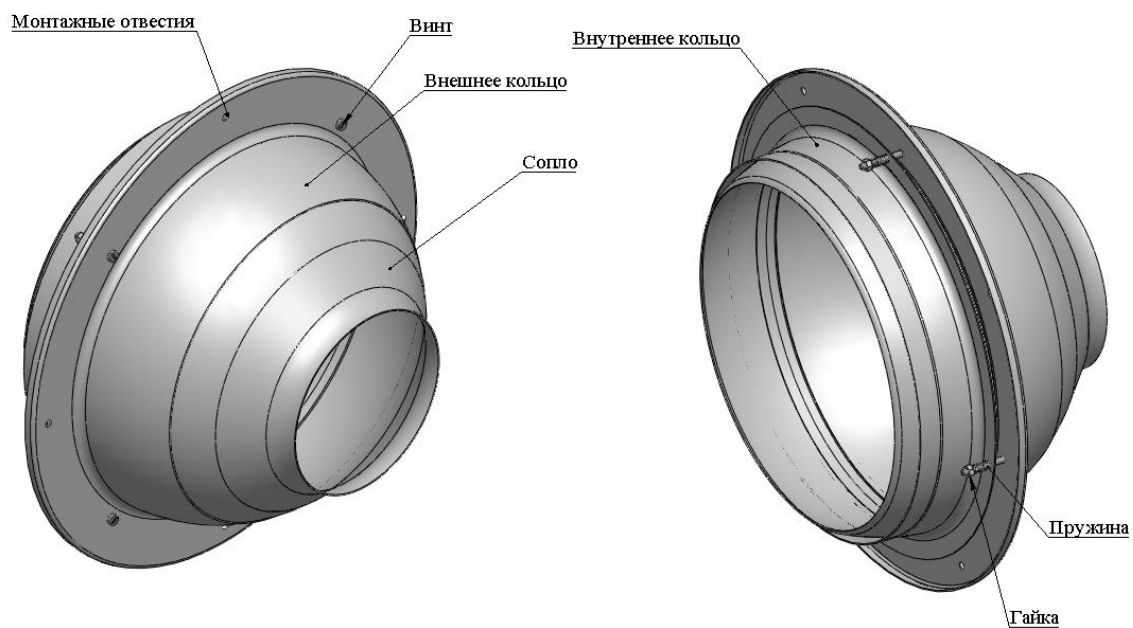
Внешний вид и конструктивные элементы 1СДК.
